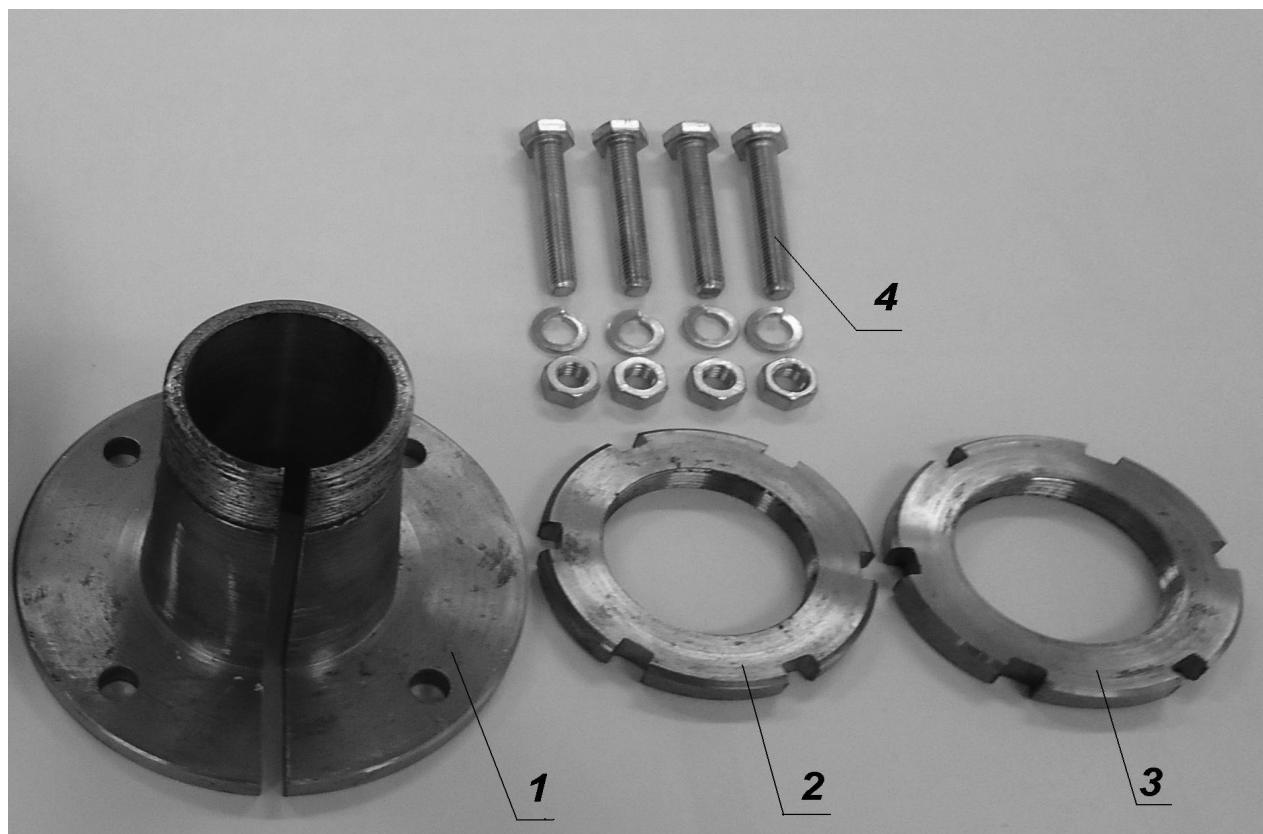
Ремонтный комплект для восстановления шпоночных соединений:
